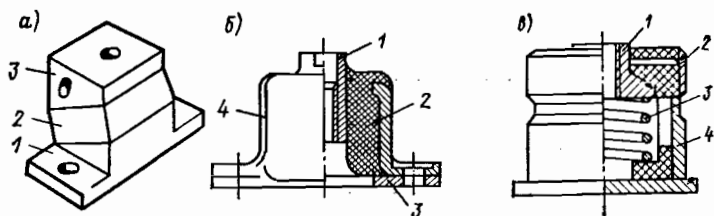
Амортизаторы: а — пластинчатый с наклонным расположением резины
